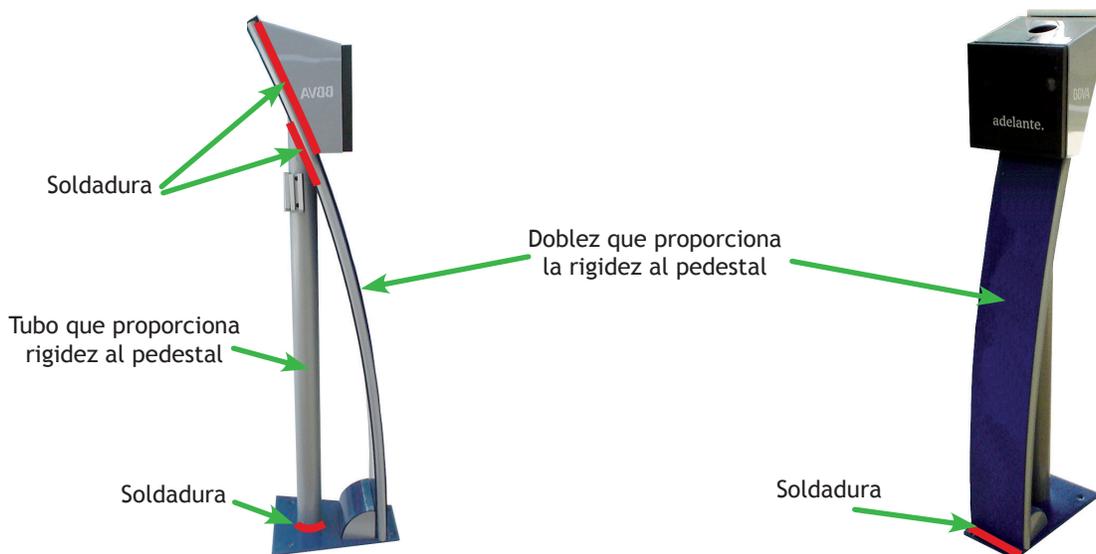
Zonas de soldadura y rigidez en pedestal
